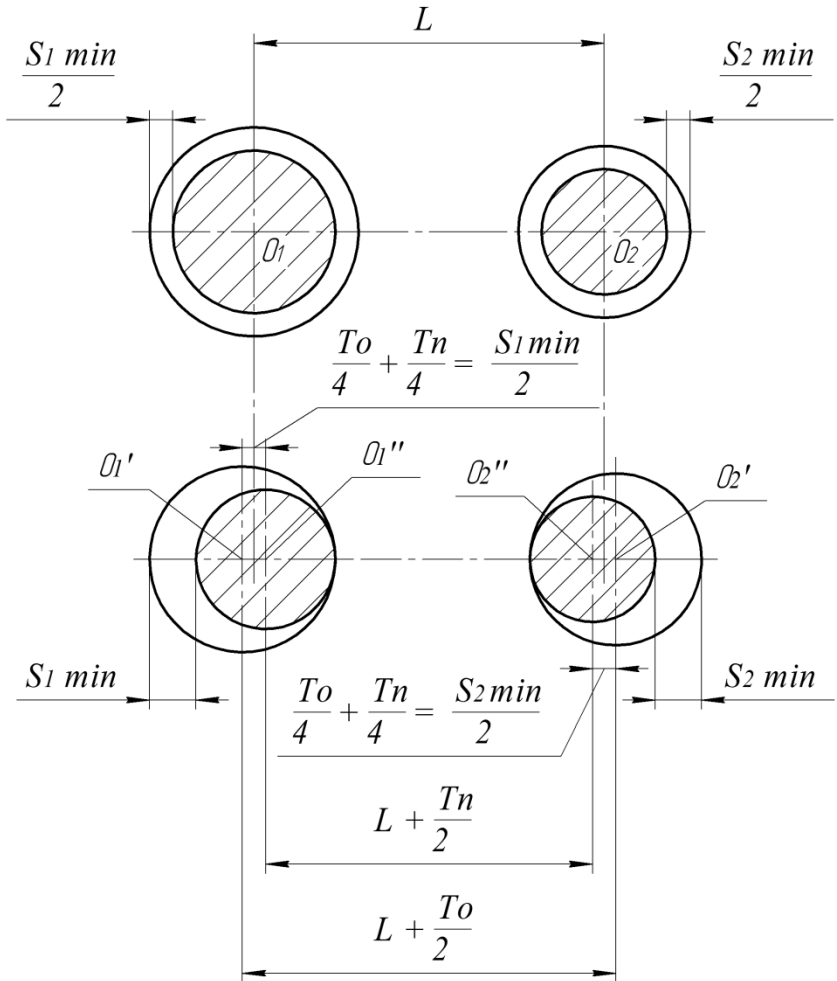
Розрахункова схема для випадку установки заготовки на площину і два циліндричних пальці
